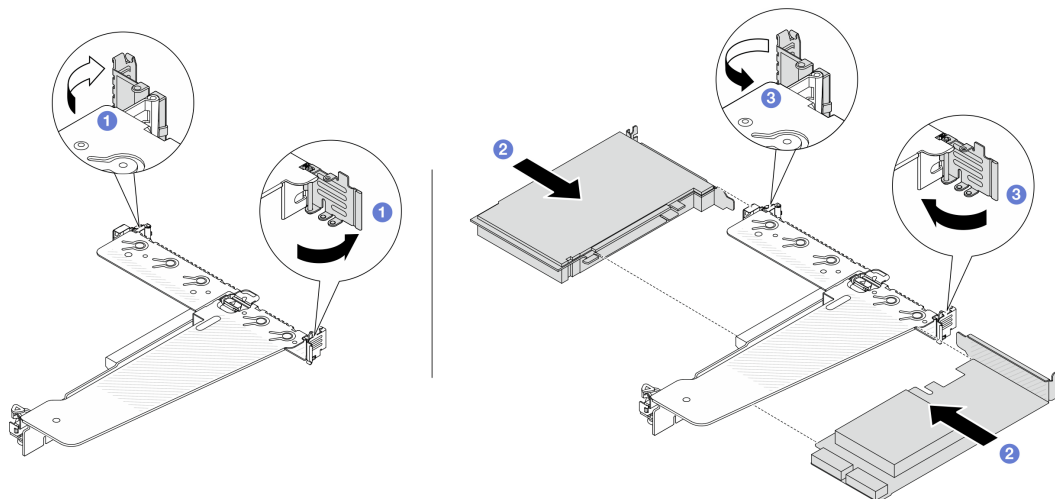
Instalação do adaptador PCIe no conjunto de placa riser LP-FH traseira
